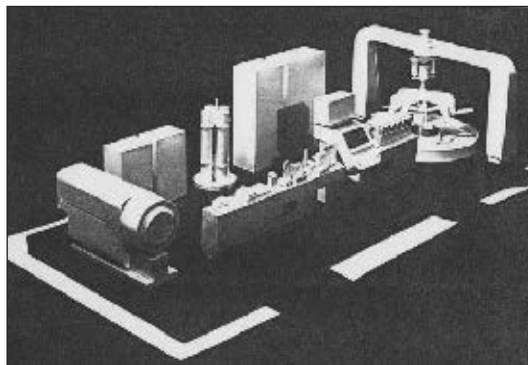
Макет промышленного образца стана АДСТ с порталом для сброса полученной трубной заготовки в корзину волочильного барабанного стана
